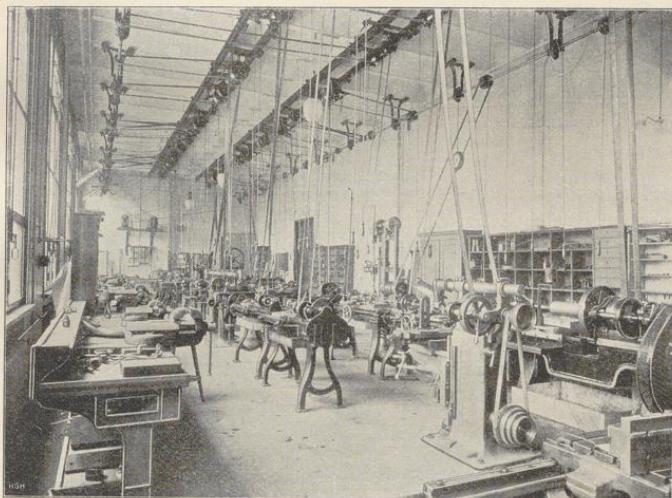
Mechanische Werkstatt W 103 Innenansicht.
